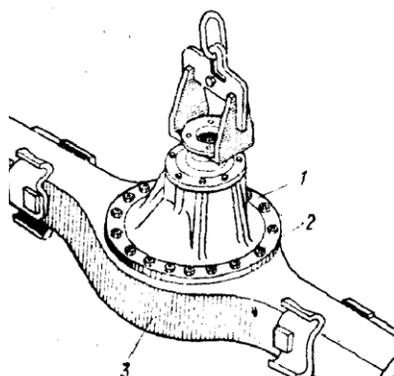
Снятие главной передачи: 1 — передача главная; 2 — гайка; 3 — корпус
